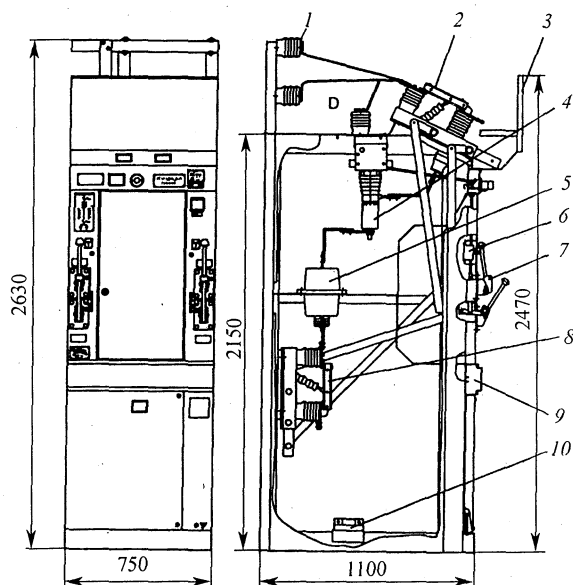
Камера КСО-298: 1 — сборные шины; 2 — разъединитель; 3 — защитный экран; 4 — выключатель; 5 — трансформаторы тока; 6 — блокиратор; 7 — приводы разъединителей; 8 — линейный разъединитель; 9 — клеммник; 10 — трансформатор тока нулевой последовательности
